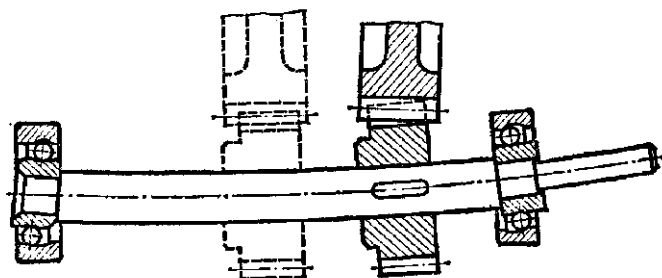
Расположение зубчатых колес относительно опор
